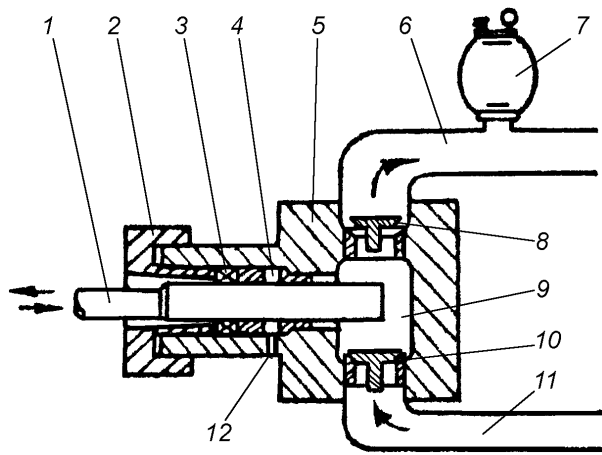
Схема плунжерного насоса: 1 – плунжер; 2 – кришка сальника; 3 – ущільнення; 4 – гідрозатвор; 5 – корпус; 6 – напірний патрубок; 7 – пневмокомпенсатор; 8 – нагнітальний клапан; 9 – робоча камера; 10 – всмоктувальний клапан; 11 – всмоктувальний патрубок; 12 – отвір подачі промивної води
